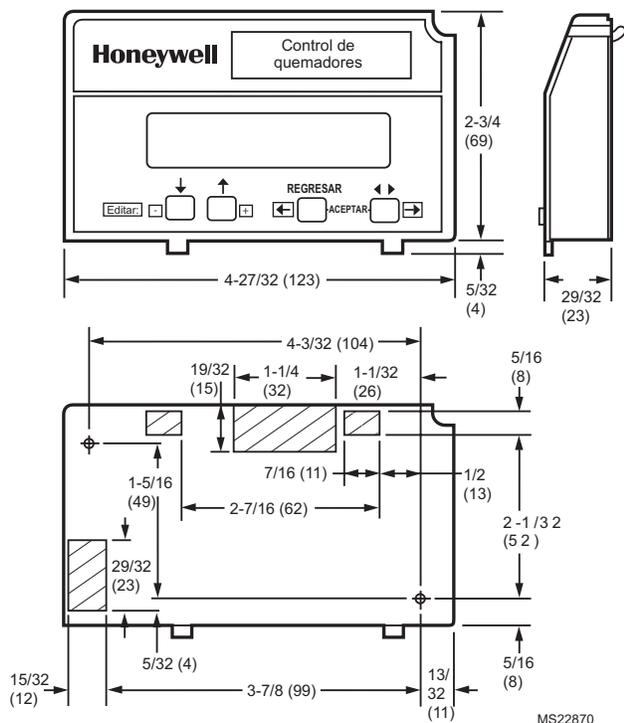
Dimensiones aproximadas de S7800A1167 en pulgadas (mm).
